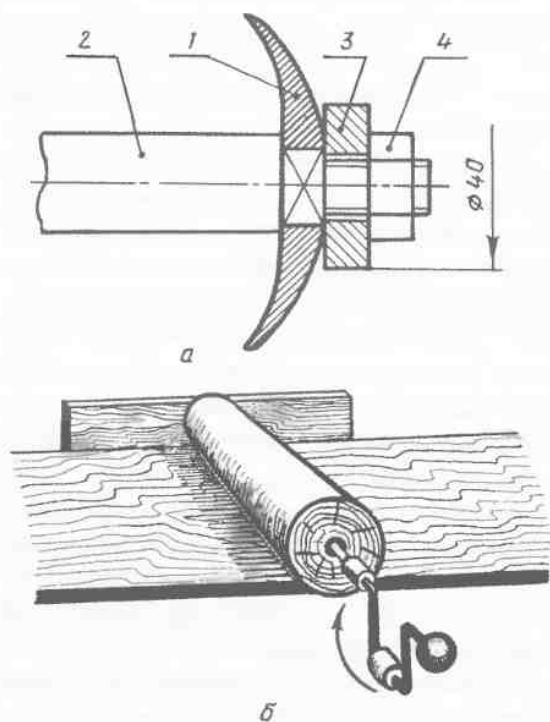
Инструмент и приспособление для расширения канала в заготовке колонны: а — фреза 1 на квадратной заточке стержня 2 с помощью направляющего кольца 3 и гайки 4; б — доска, прибитая к торцу заготовки колонны (обеспечивает ей устойчивость при силовых вращениях коловорота)
